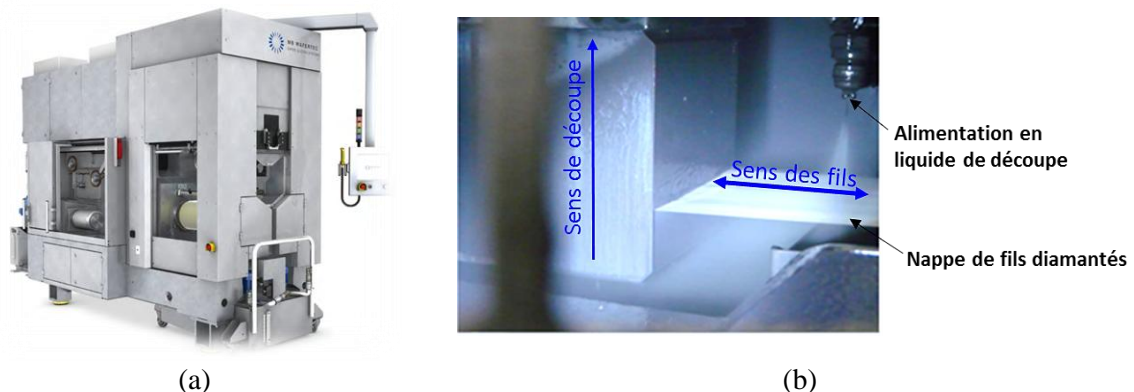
Photographies illustrant le procédé de découpe DW : (a) machine de découpe commercialisée par « Meyer-Burger » ; (b) brique de silicium monocristallin en cours de découpe.
